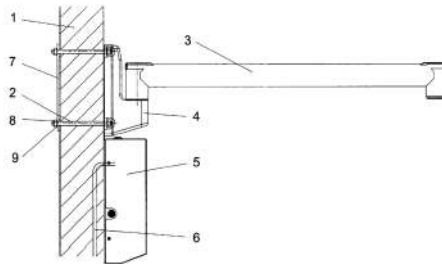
Bauteile Wandbefestigung mit Gegenplatte
